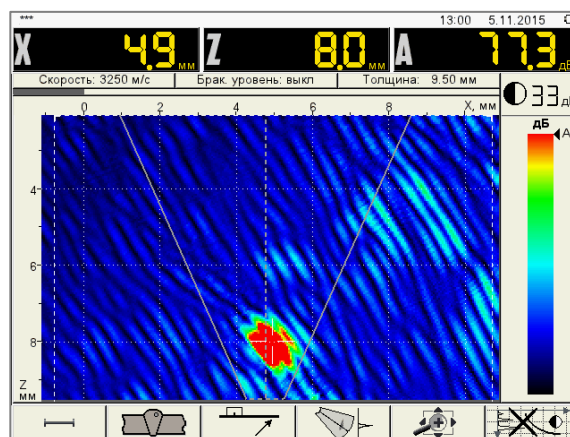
Дефект сварного шва, выявленный при УК.
